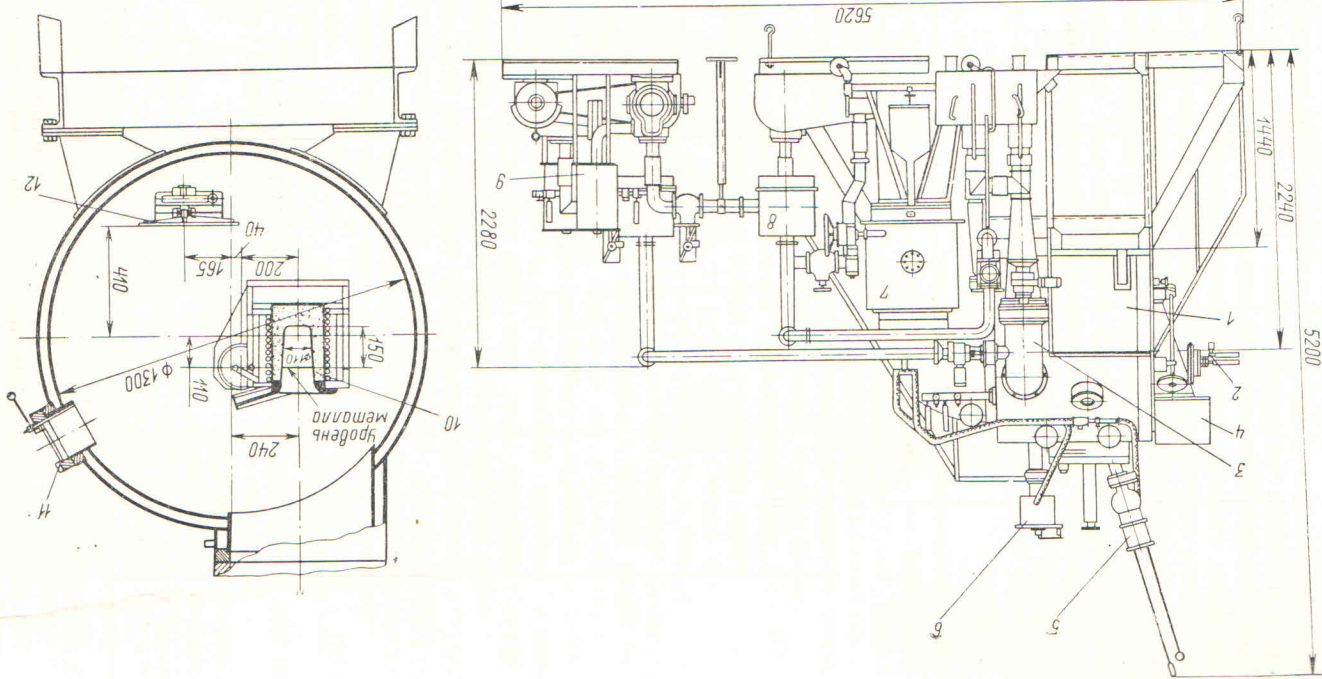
Схема вакуумной индукционной печи ИСВ-0,01 ПИП. 1 — планчатая камера; 2 — ввод электродпитания; 3 — вращательный насос ВН2000; 4 — механизм наклона печи; 5 — устройство для измерения температуры и взятия проб; 6 — дозатор; 7 — вакуумный аппарат ВА-8-4 ПП; 8 — фильтр; 9 — вакуумный насос ВН-4Т; 10 — индукционная печь; 11 — смотровое окно; 12 — стом для установки изложниц
